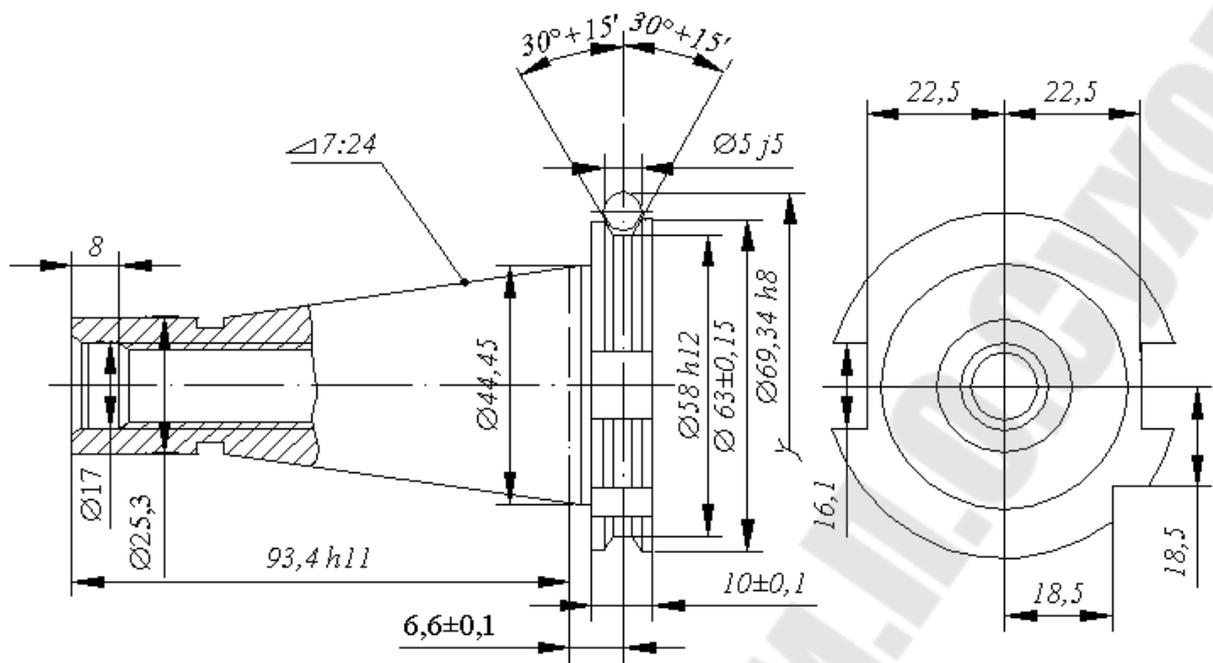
Инструментальные оправки с конусом 7:24 для автоматической смены инструмента в сверлильно-фрезерно-расточных станках.
